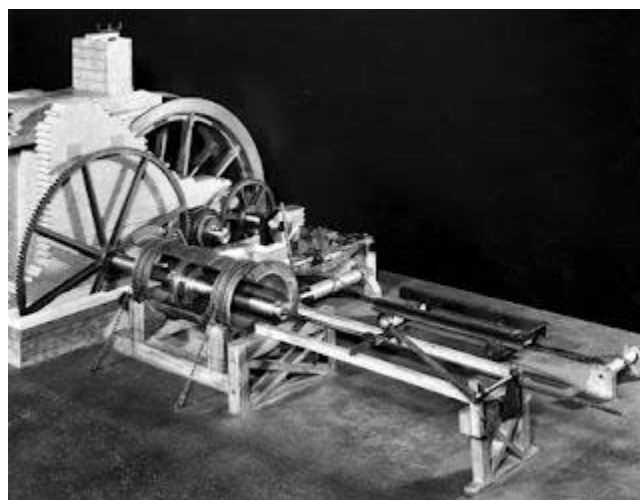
Mandrinadora de John Wilkinson (1775). Fuente: Alma de herrero. Máquinas herramientas. <http://2.bp.blogspot.com/>
